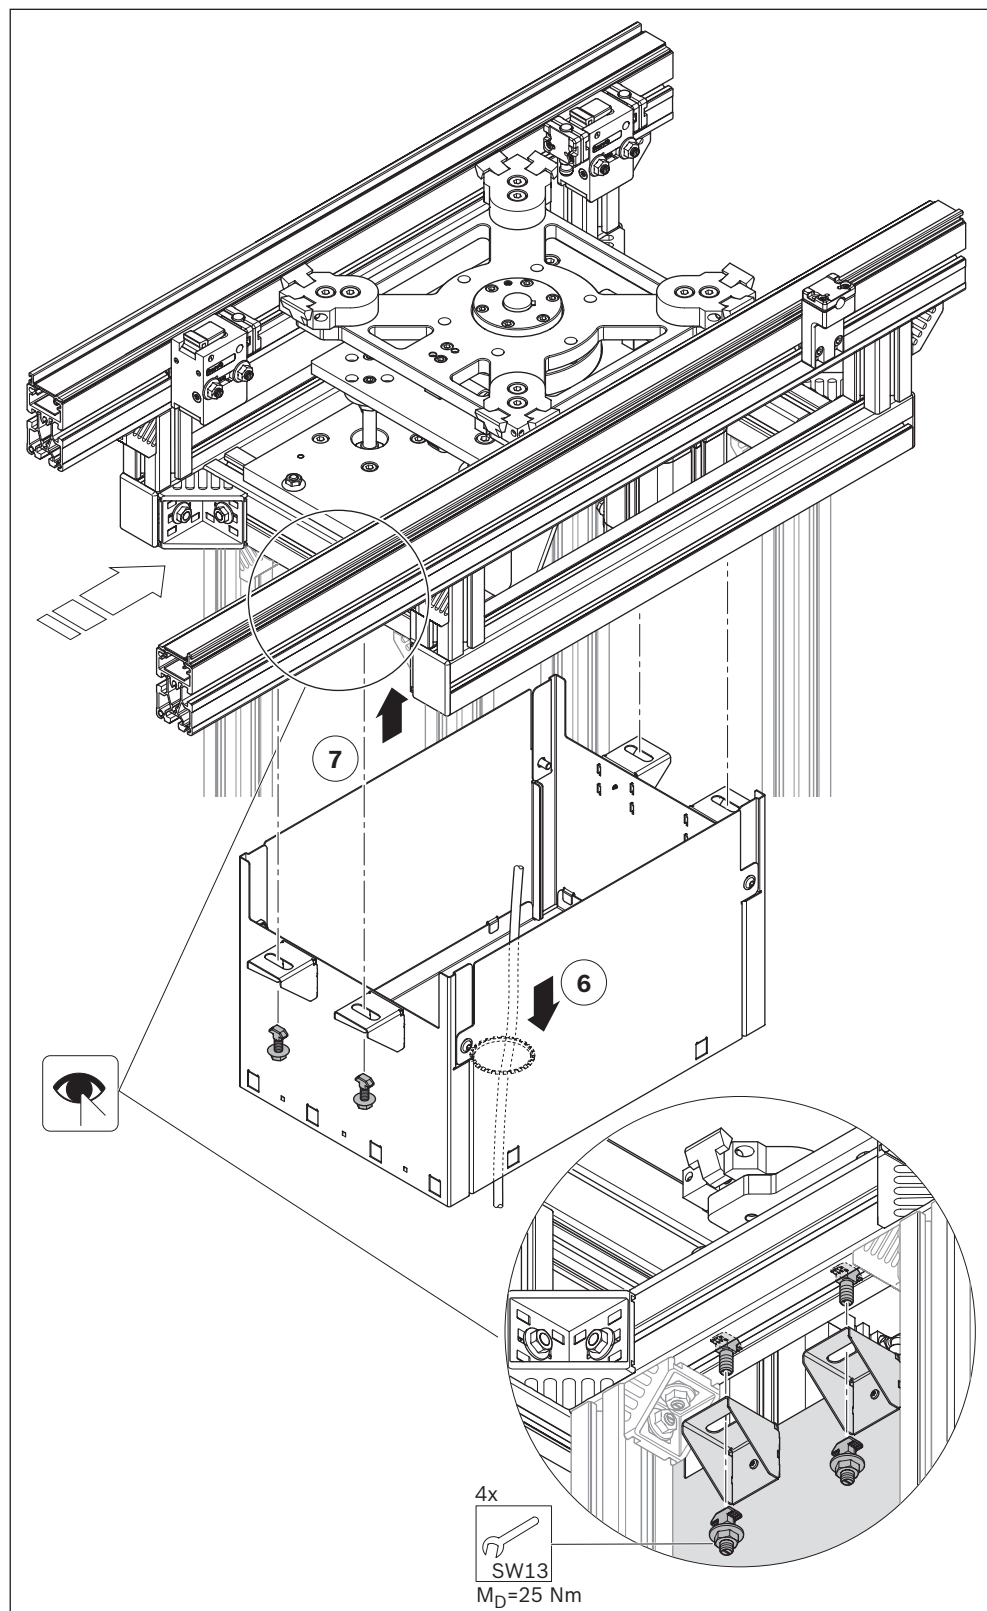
Montaje de la caja de protección (aquí tamaño constructivo 2 180° para WT 2, WT 2/F)
